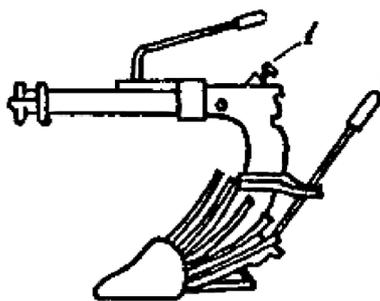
Схема регулируемого корпуса плуга с винтовым механизмом:
